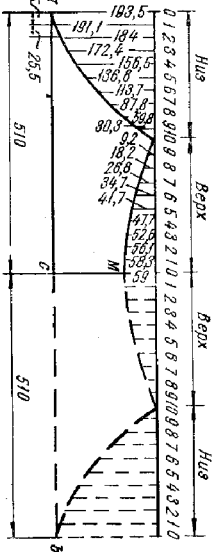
Разметка коша трубы II разветвленного сварного тройника (штамп).
